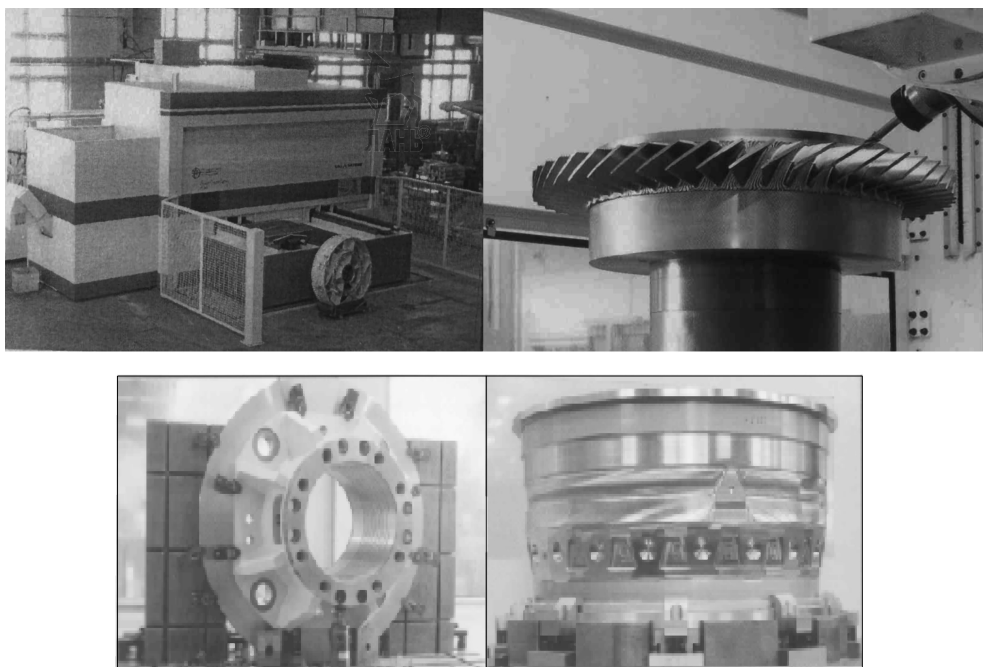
Портальный продольно-фрезерно-расточной обрабатывающий центр
